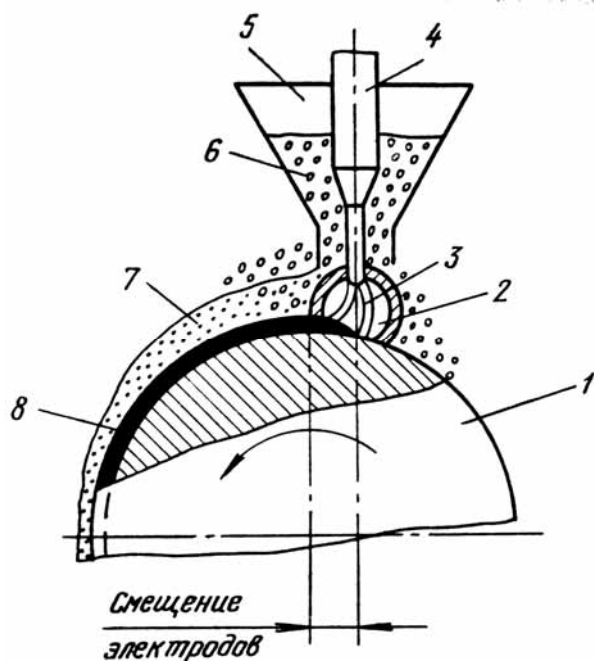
Схема установки автоматической наплавки под слоем флюса:
